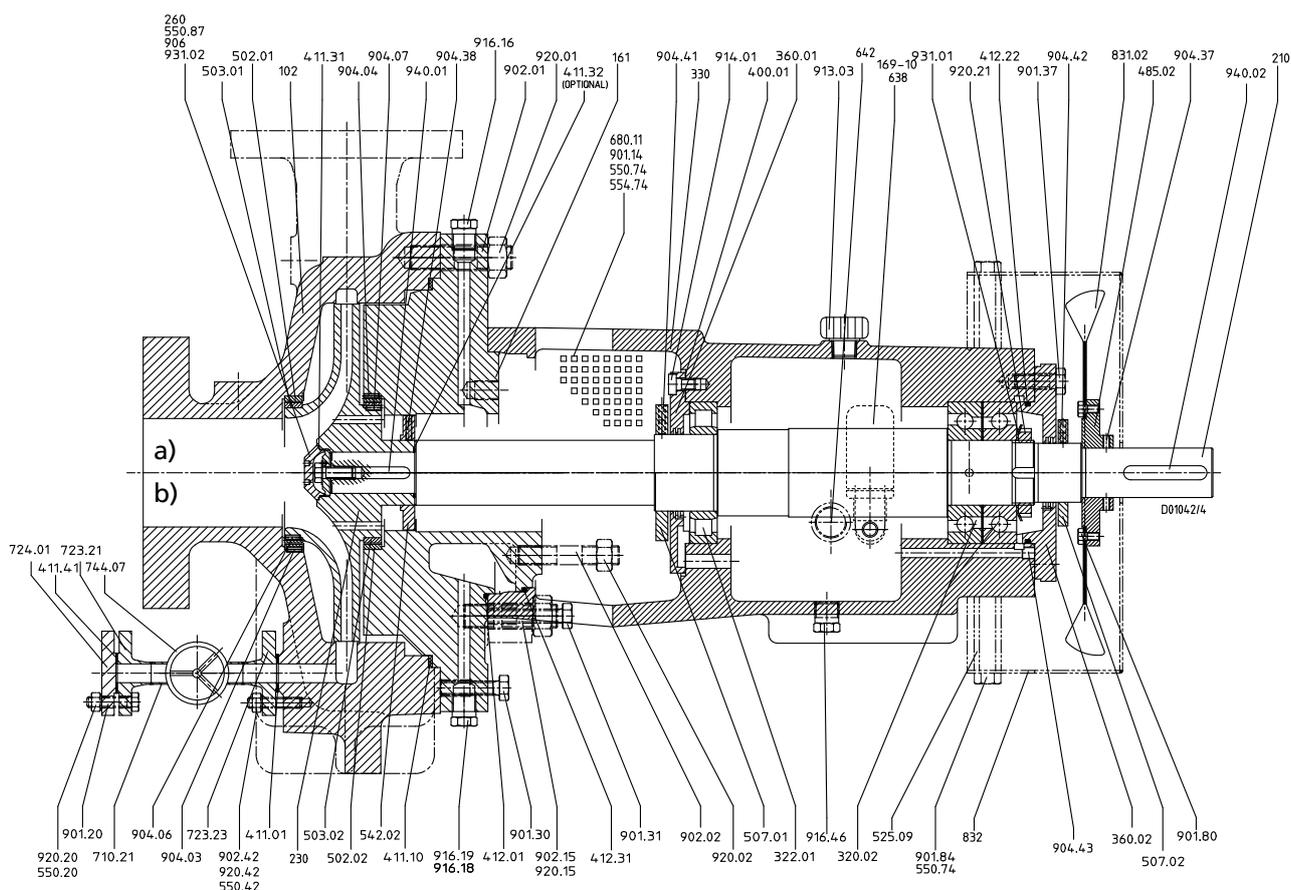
Корпус подшипников V06 и V07, а) без охлаждения и б) с охлаждением
